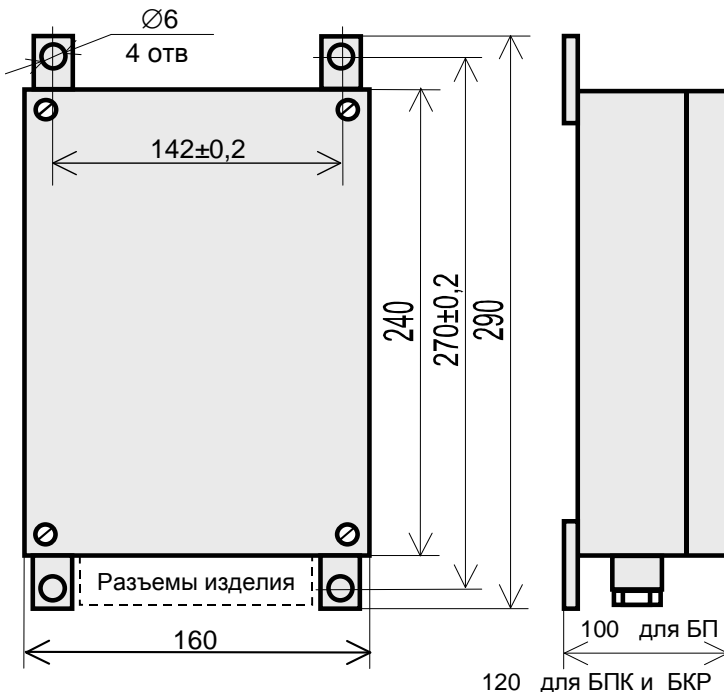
Габаритные и присоединительные размеры БП, БПК и БКР
